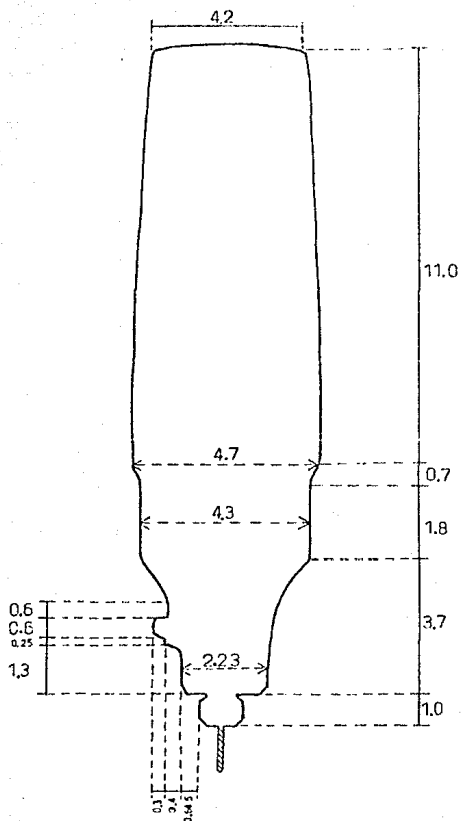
CONTORNEO DEL TALADRO O MOTO-TOOL.
